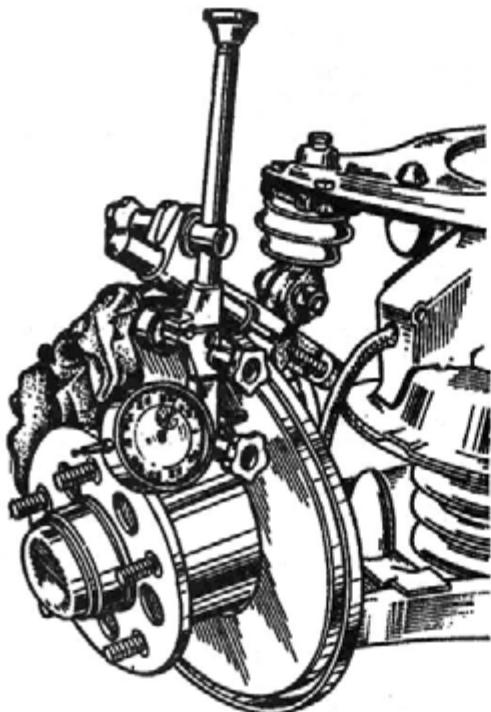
Проверка биения рабочих поверхностей тормозного диска
